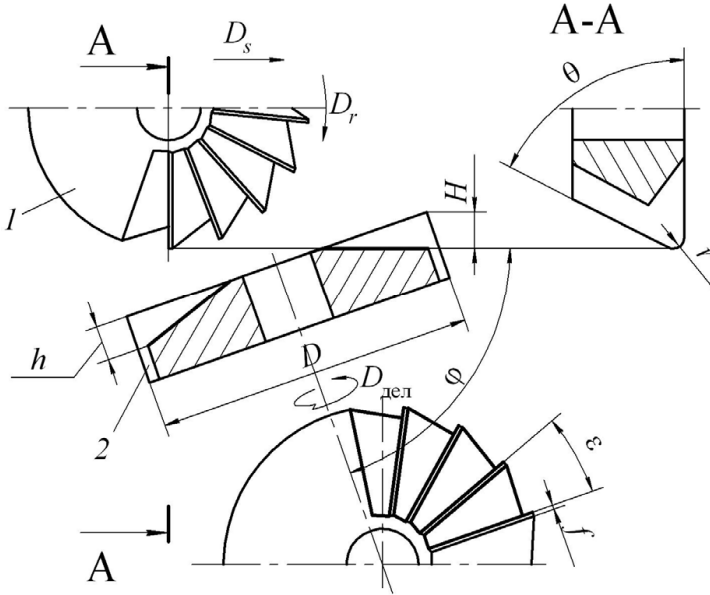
Установка заготовки при фрезеровании стружечных канавок на торцевой поверхности: 1 – инструмент; 2 – заготовка
